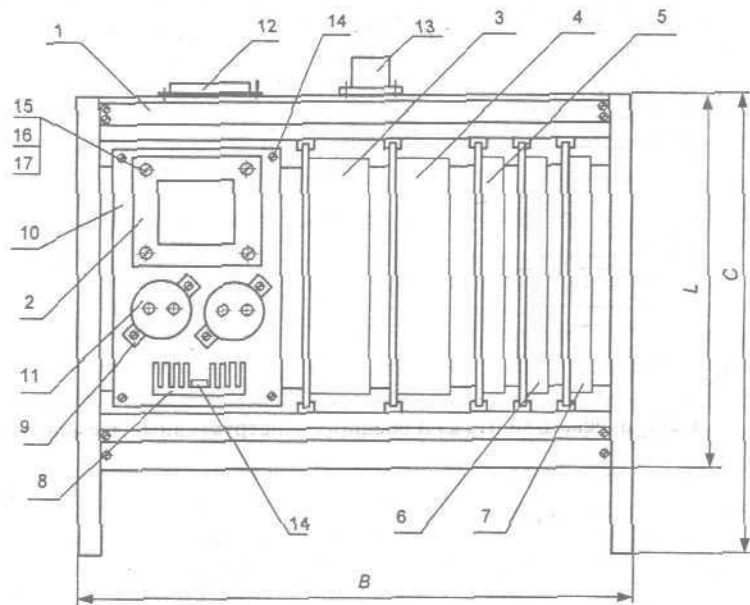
Фрагмент чертежа общего вида ЭБ:
